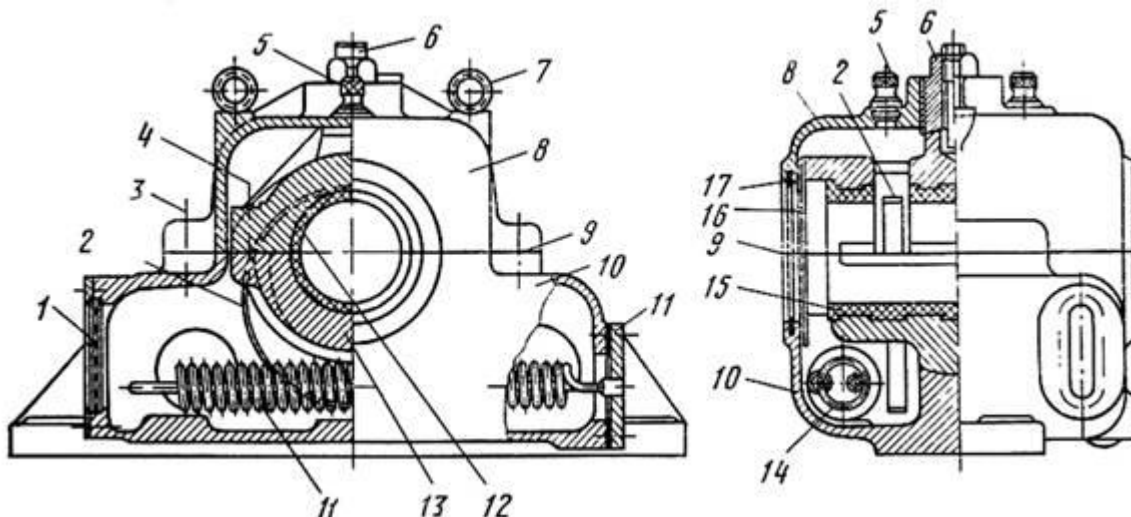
Подшипник дымососа с самоустанавливающимися вкладышами и кольцевой смазкой
